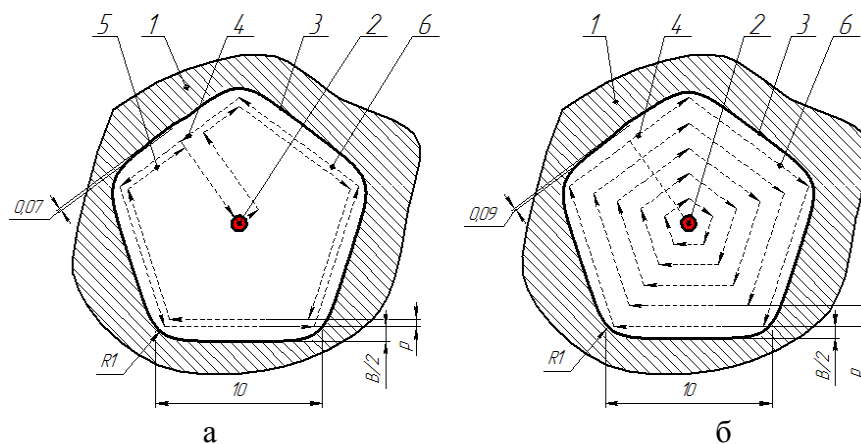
Схема обработки отверстия пятиугольного поперечного сечения; (а) - обработка за два прохода; (б) - обработка с удалением всего материала внутри контура; 1 – обрабатываемая деталь; 2 – ПЭИ; 3 – обрабатываемая поверхность детали; 4 – направление перемещения инструмента; 5 – траектория ПЭИ при черновой обработке; 6 – траектория ПЭИ при чистовой обработке; p – шаг проходов, $B/2$ – полуширина реза
